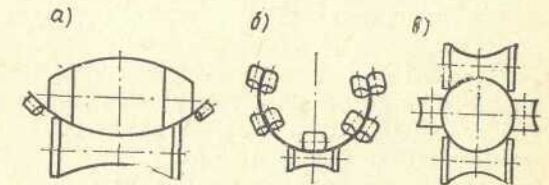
Контактная сварка труб методом сопротивления
